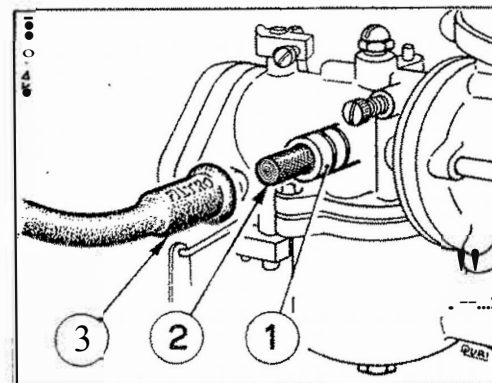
SMONTAGGIO DEL FILTRO SUL CARBURATORE
